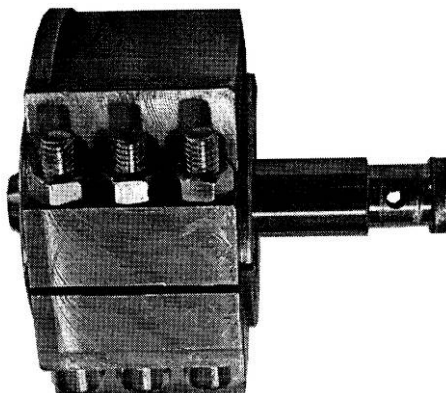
Установка вала во втулку перед запрессовкой
